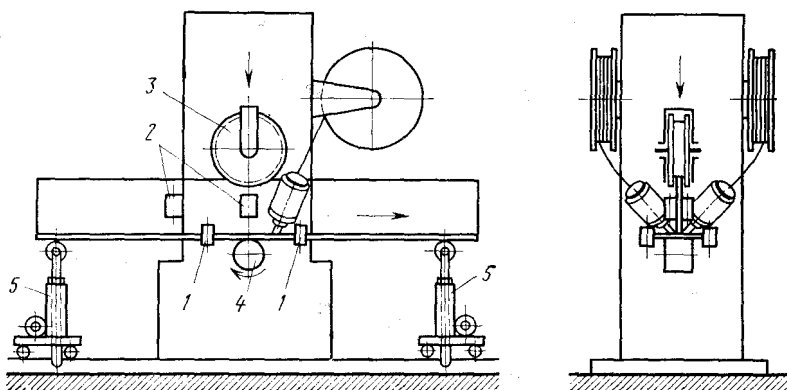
Схема станка для сварки балок таврового профиля
